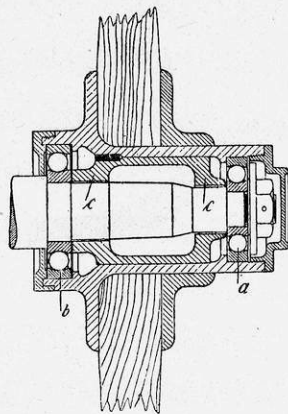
Втулка передняго колеса съ шариковымъ подшипникомъ (въ разрѣзѣ).
